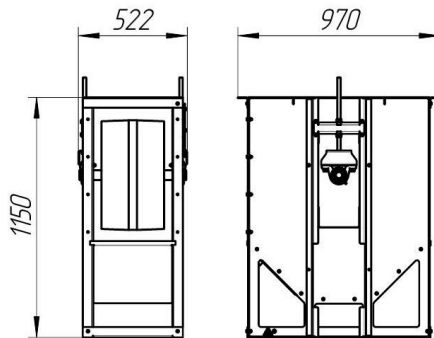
Станция натяжная нории Н-50. Размеры габаритные
